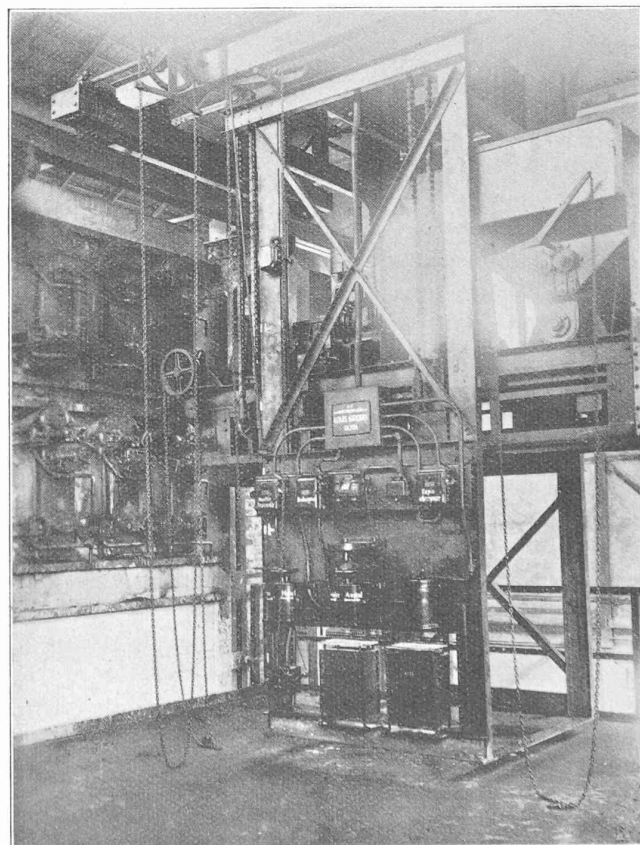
Le four, côté enfournement, et la machine à charger.
